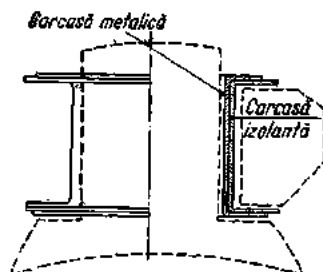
Carcasă metalică și izolanță pentru bobine polare.
